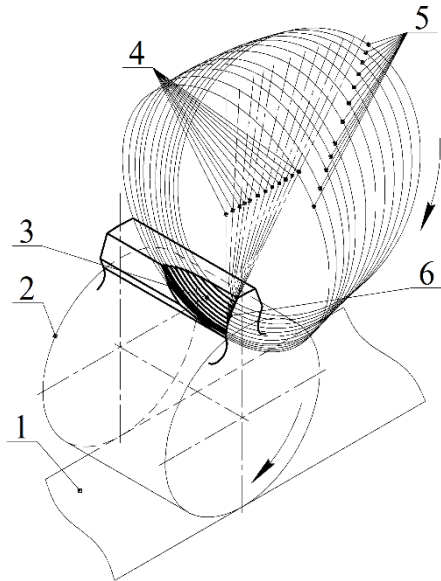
Утворення евольвентного профілю при черв'ячно-контурному зубофрезеруванні, схема руху точки РК, яка описує оброблювану евольвентну поверхню
